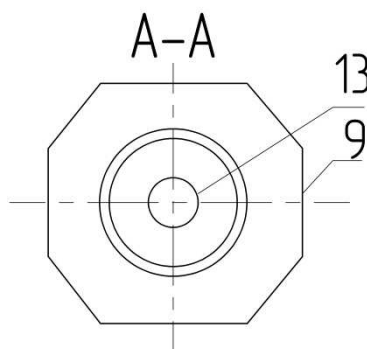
Съёмный фланец с натяжным устройством для натяжения струны
